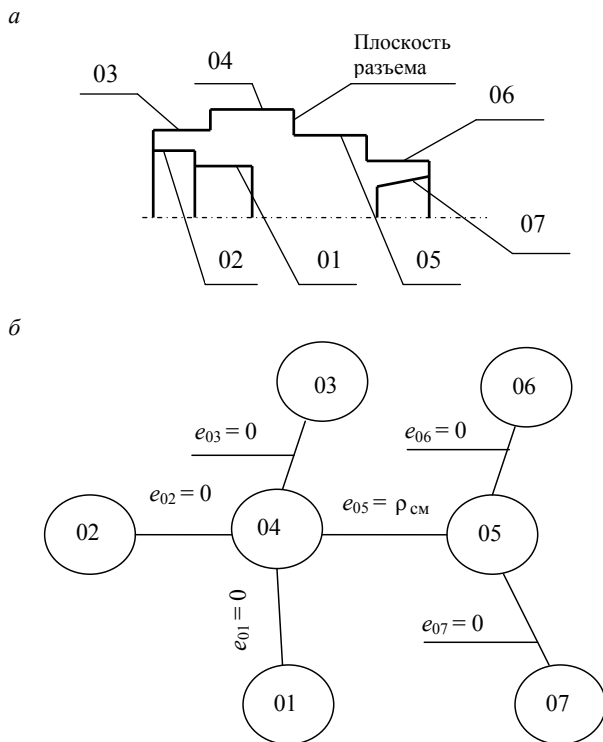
Заготовка и дерево ее эксцентриситетов
